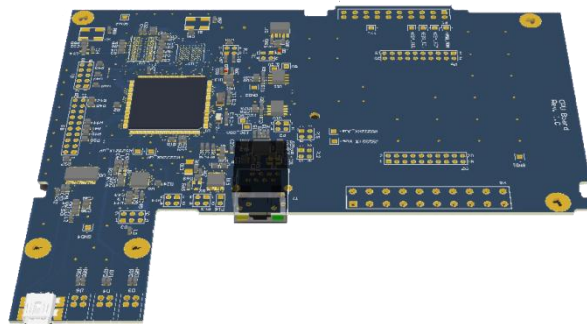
PCB CPU diseñado y fabricado para la construcción del prototipo.
